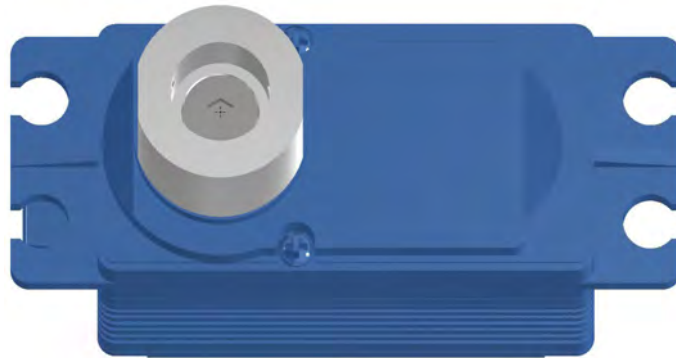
Servomotor atornillado a pieza de aluminio para transmisión de torque. Fuente propia.
